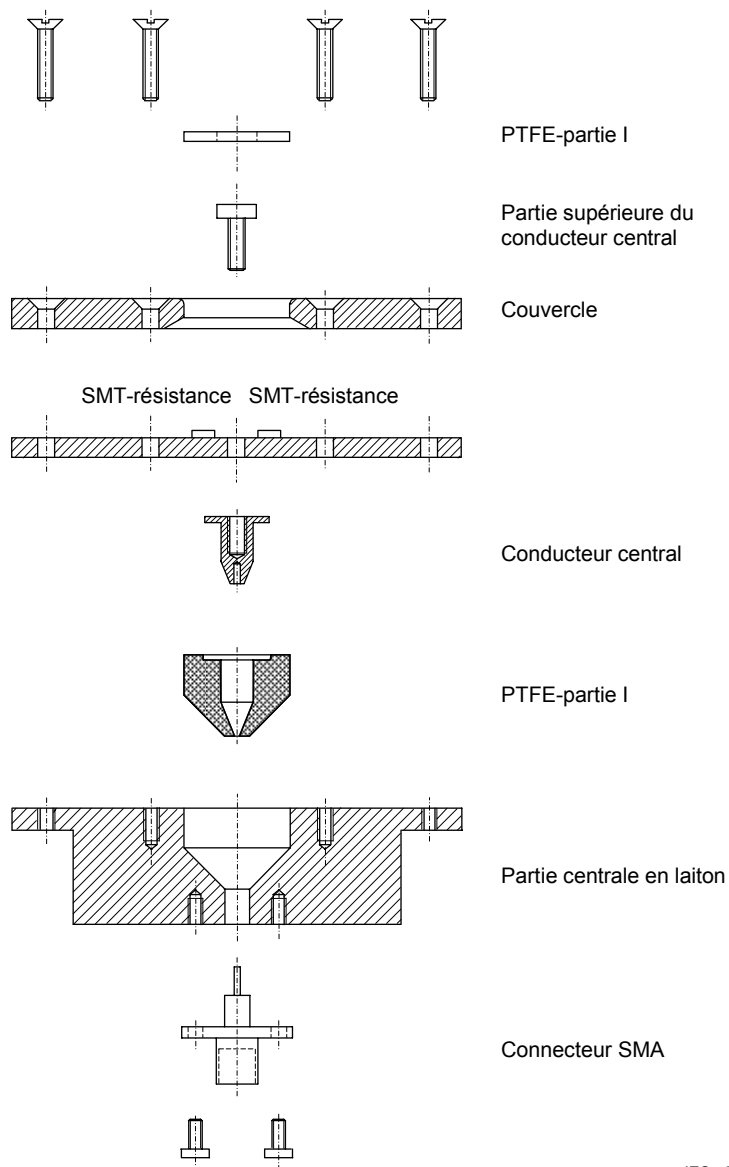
Dessin mécanique d'une cible coaxiale (dessin 3 sur 5)
